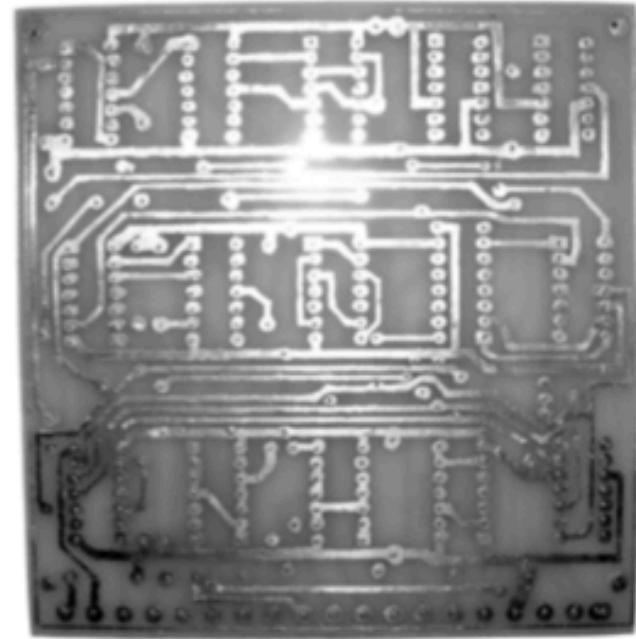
Заготовка платы для ключа с памятью Е. Кургина (UG6AD). Вид со стороны, изготовленной по-старинке – вручную
